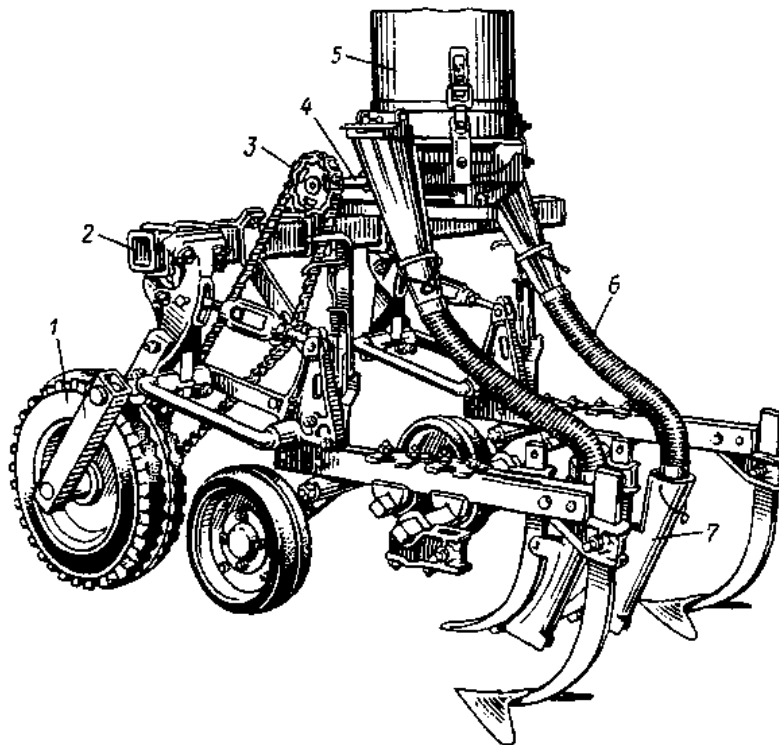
Підживлювальне пристосування: 1 - опорне колесо; 2 - рама; 3 - механізм приводу; 4 - приводний валик; 5 - туковисівний апарат; 6 - тукопровід; 7 - підживлювальний ніж
